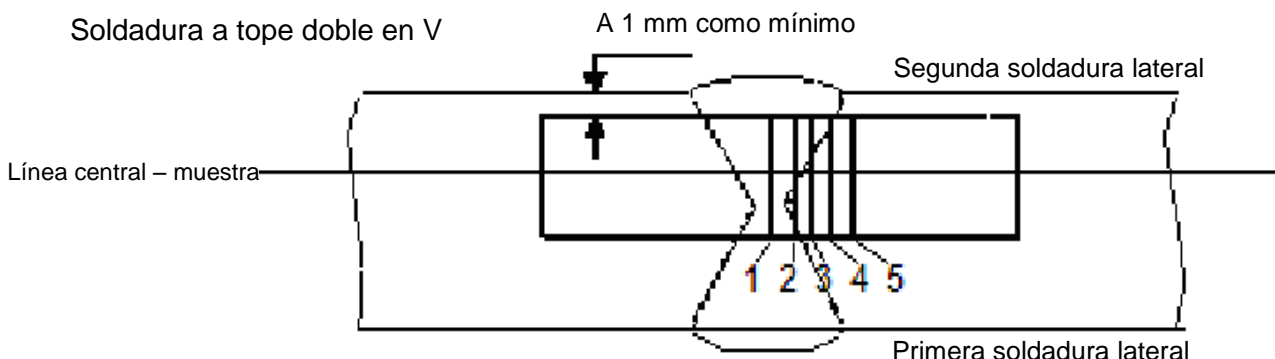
Orientación de la muestra de prueba de la soldadura
